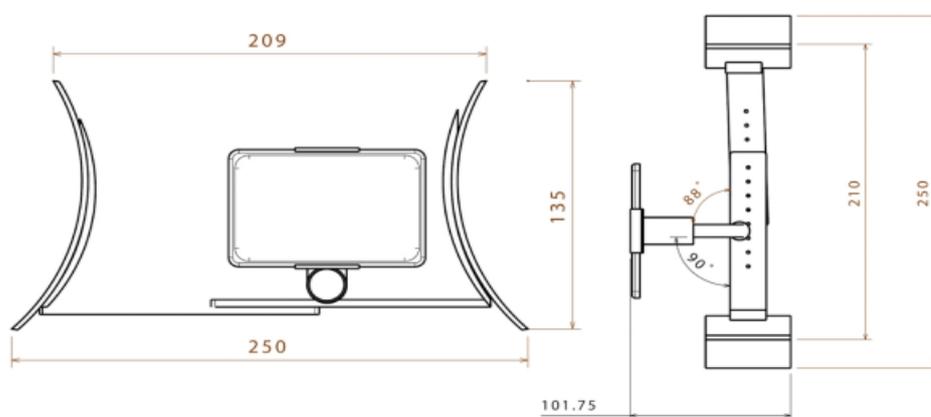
Desenho técnico do Posicionador de membros inferiores
